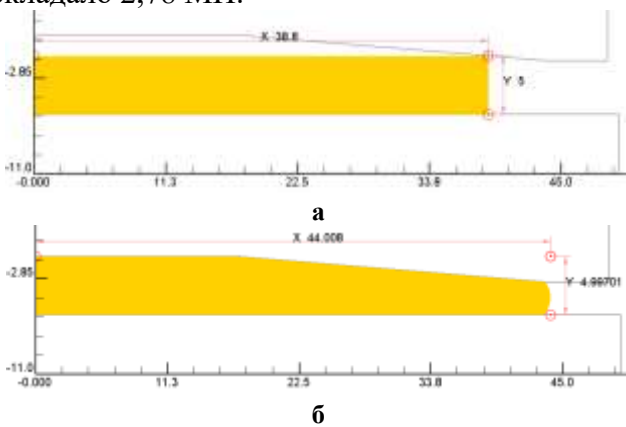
Розрахункова схема процесу гарячого профілювання заготовки:
